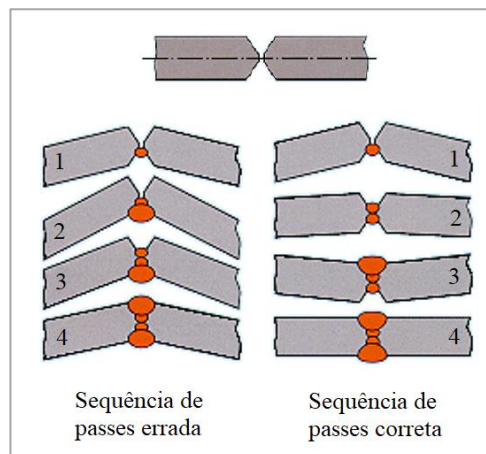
Seqüências de soldadura, alternando ou não, lateralmente os passes - [10] Imagem adaptada
